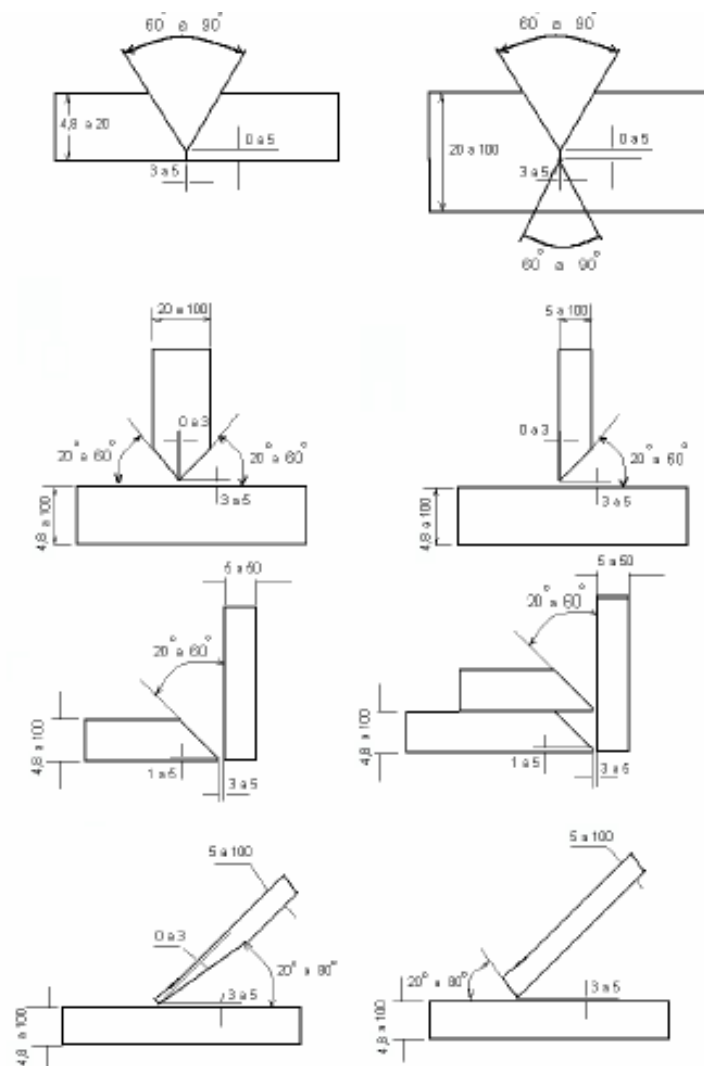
; Detalhes dimensionais das juntas soldadas
